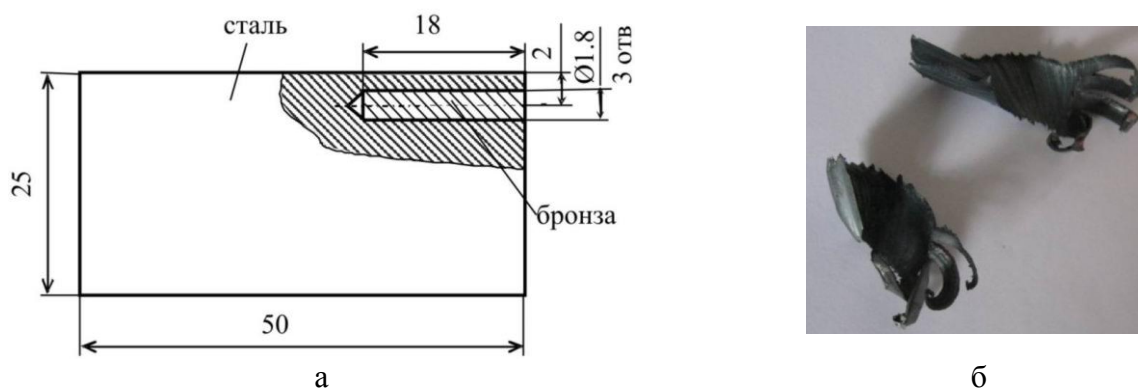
Спеціальна заготовка зі сталі 45 з бронзовими стрижнями (а) та стружка при одночасній обробці сталеві заготовки і бронзових стрижнів (б)
